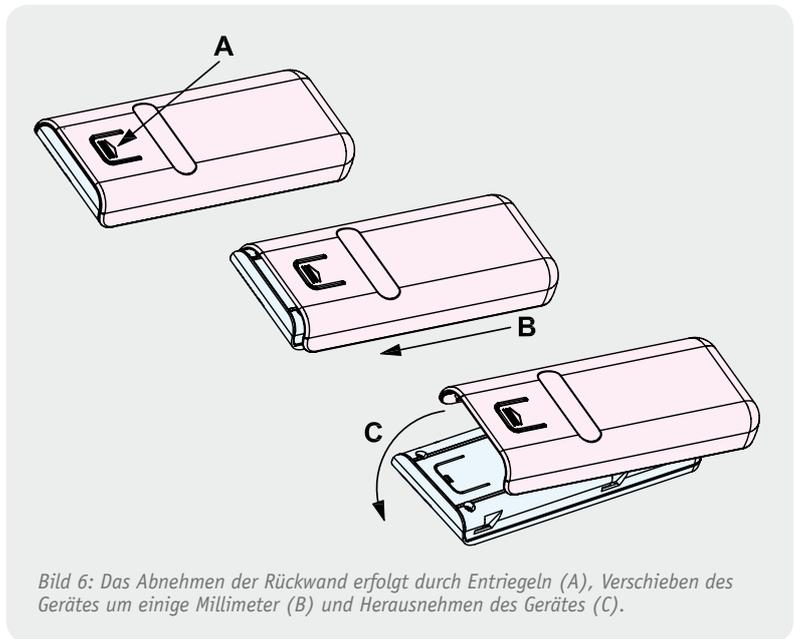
Das Abnehmen der Rückwand erfolgt durch Entriegeln (A), Verschieben des Gerätes um einige Millimeter (B) und Herausnehmen des Gerätes (C).
